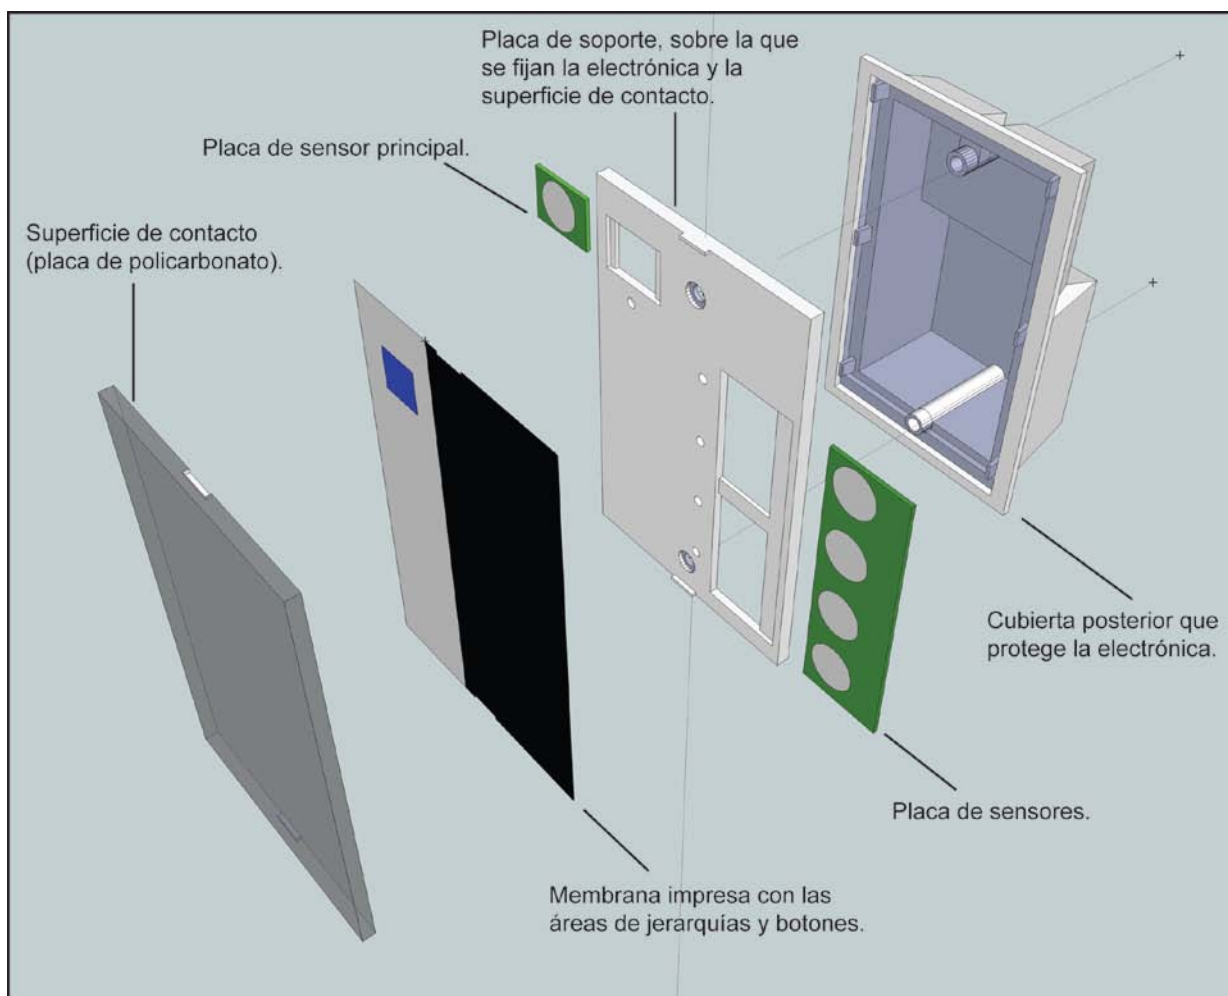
Despiece del módulo principal con la descripción de cada uno de sus componentes.
